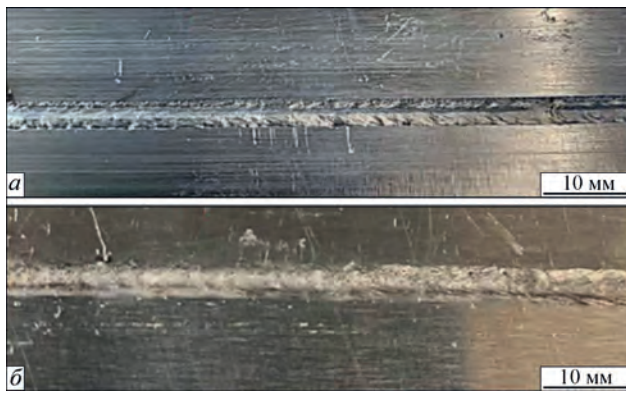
Зовнішній вигляд зварних з'єднань сплавів 5251 з 6082 [30] (товщина 1,5 мм) у виробках TWB (tailored welded blanks), одержаних електронно-променевим (а) і лазерним (б) способами
